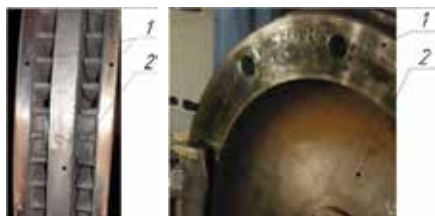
Опытный образец тормозного диска 798, предназначенный для установки на колесо
